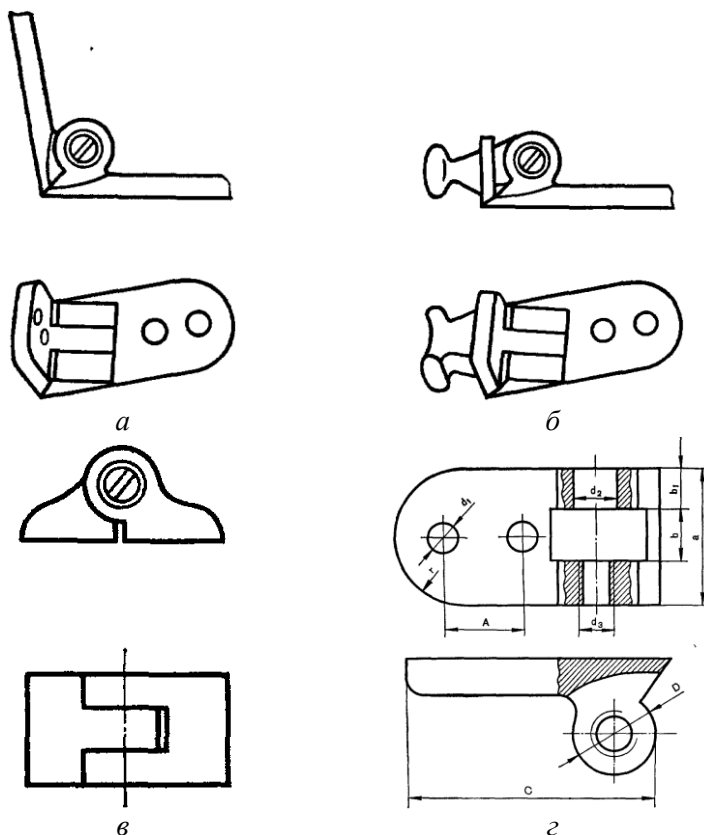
Конструкция шарниров для оправы корригирующих очков: *а* – накладной шарнир с креплением под заклепки; *б* – гарпунный шарнир; *в* – накладной шарнир с креплением сваркой или пайкой; *г* – створки накладных шарниров
